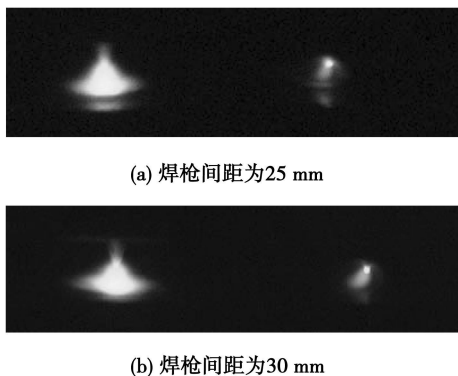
双弧 AA-TIG 焊时的电弧形貌
